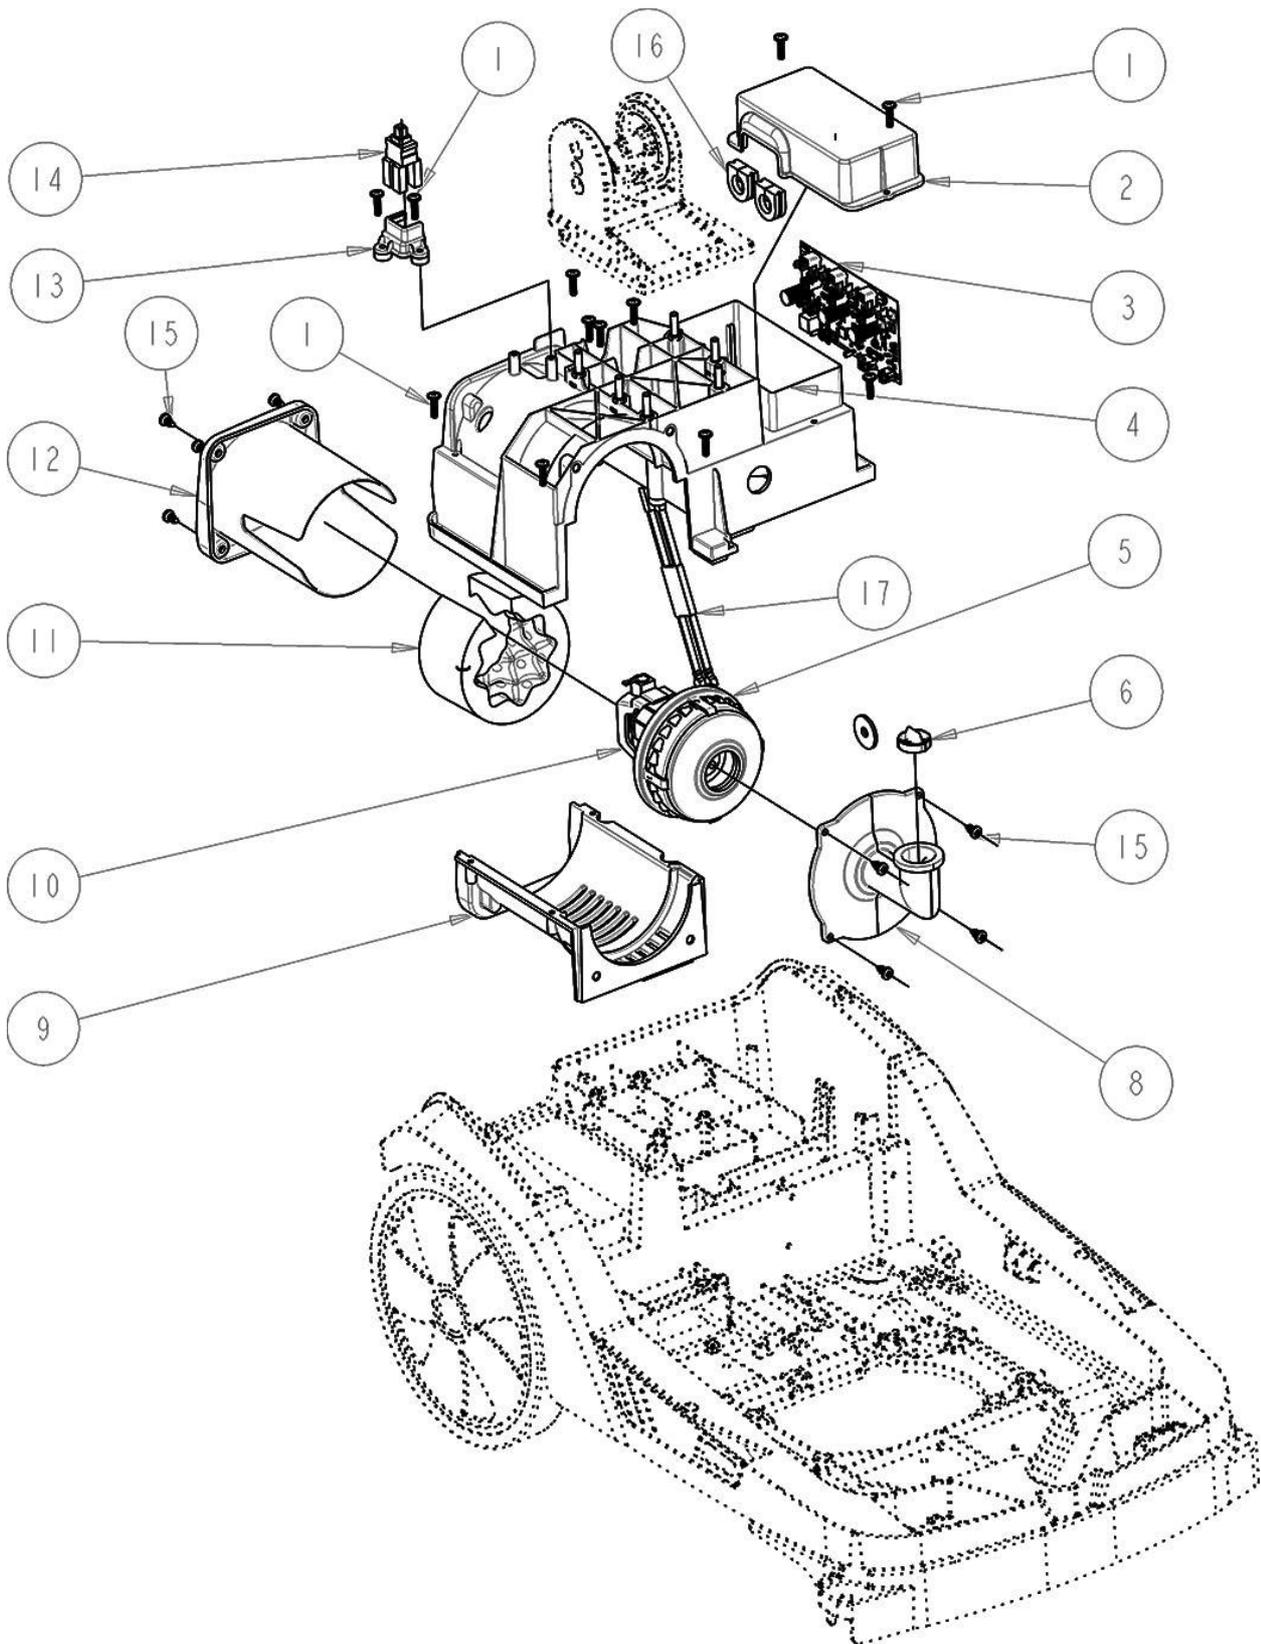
Ersatzteilzeichnung 6: Saugmotor
